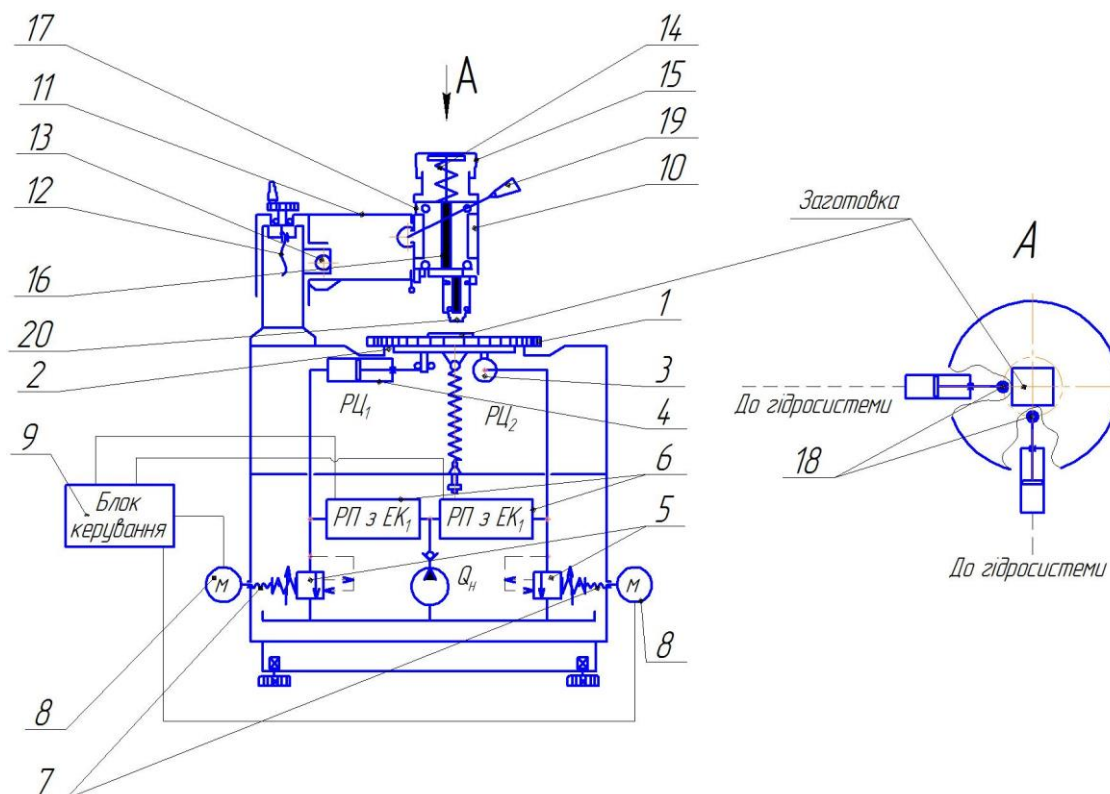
Кінематична схема гідрофікованого верстата: РП з ЕК – регулятор потоку з електромагнітним клапаном керування
